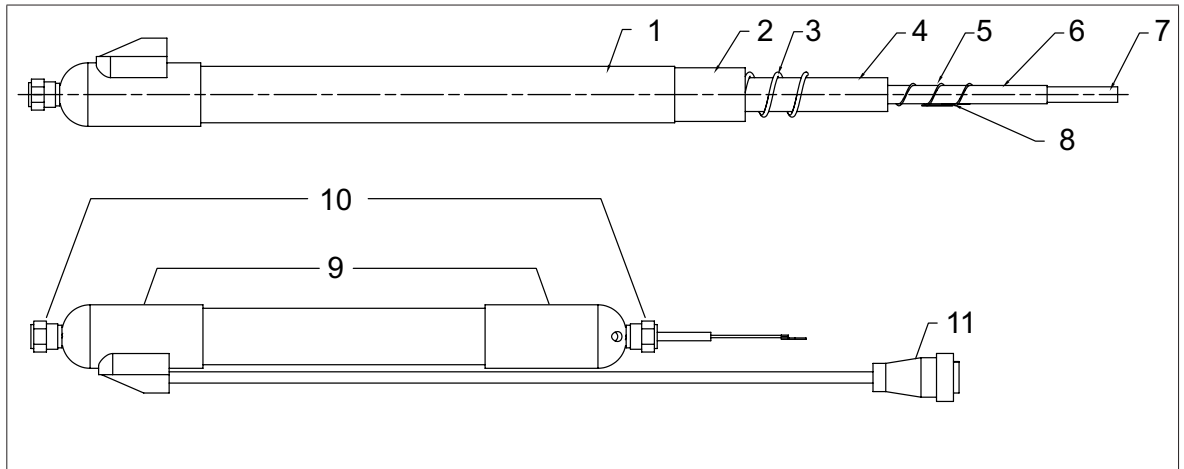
/5: Mechanische montage van de slang (versie rups)
